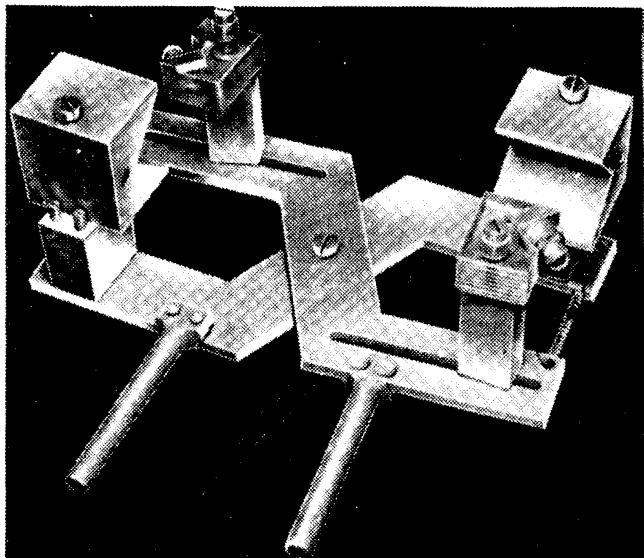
Рис. I Механическое устройство для установки искателей на контролируемое сварное соединение
